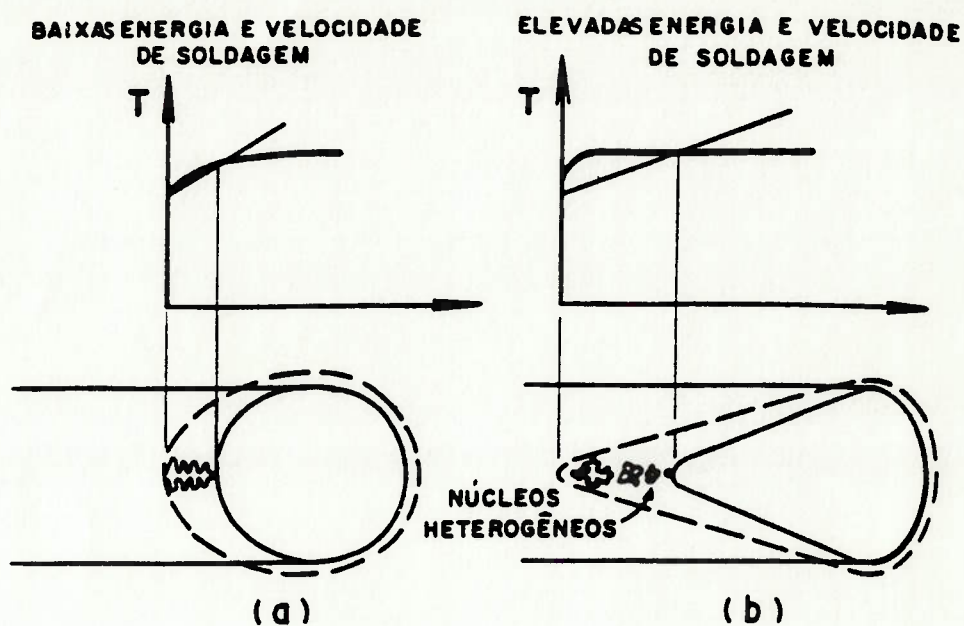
Super-resfriamento constitucional na frente de solidificação durante a soldagem [69]
